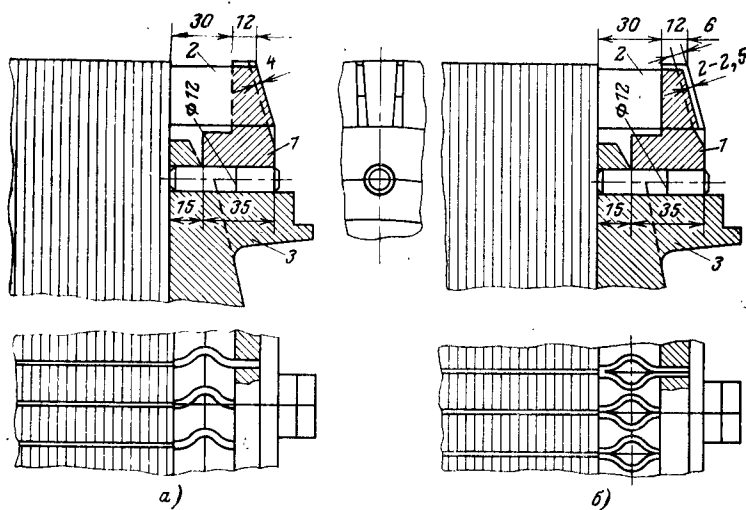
Усовершенствование конструкции обмотки ротора двигателя серии ГАМО.
